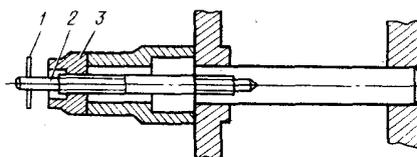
Съемник для выпрессовки оси блока шестерен заднего хода.
